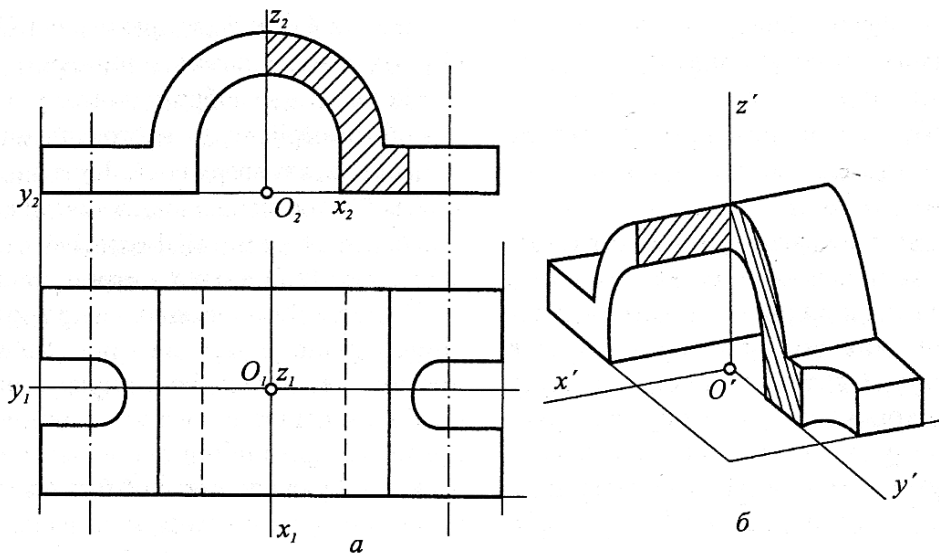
a* – вид спереду, вид зверху деталі; *б* – аксонометрія деталі в Π_3
